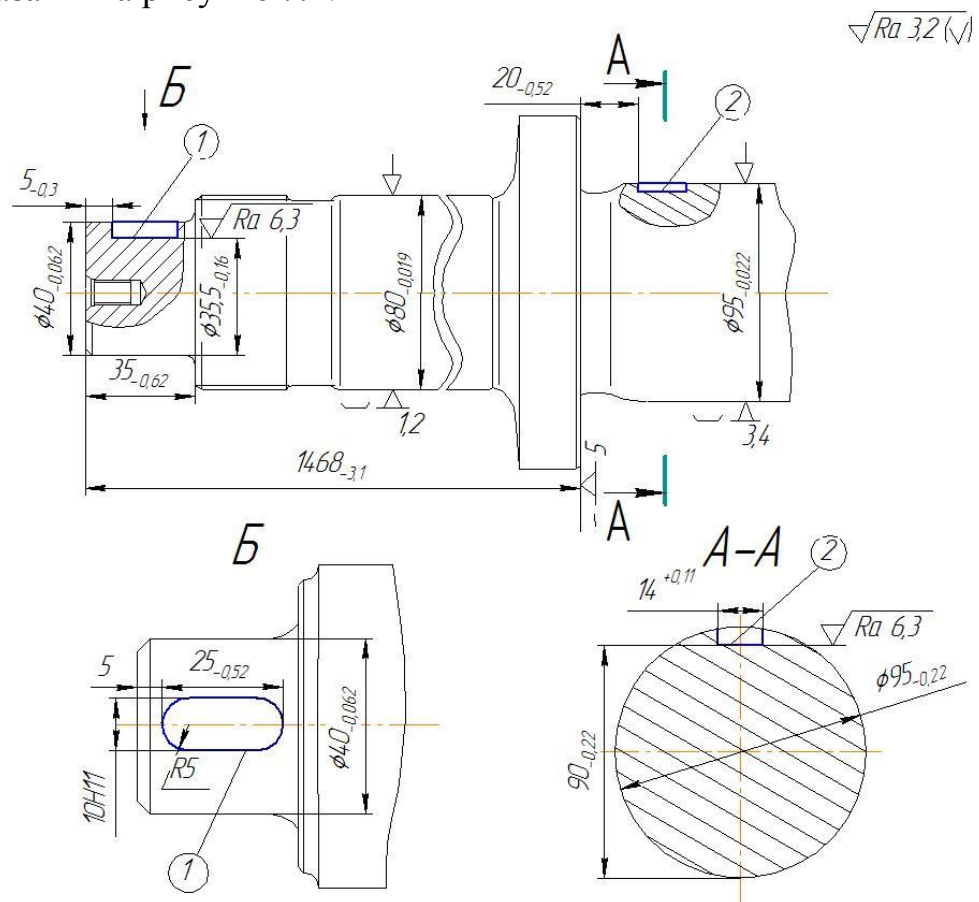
Эскиз вертикально-фрезерной операции
